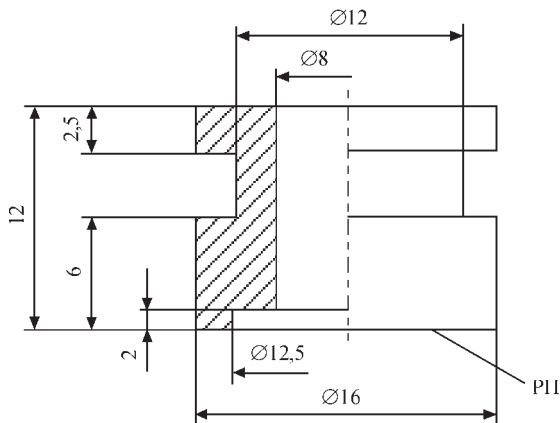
Зразок для випробування: втулка (40Х); Р11 – робоча поверхня
